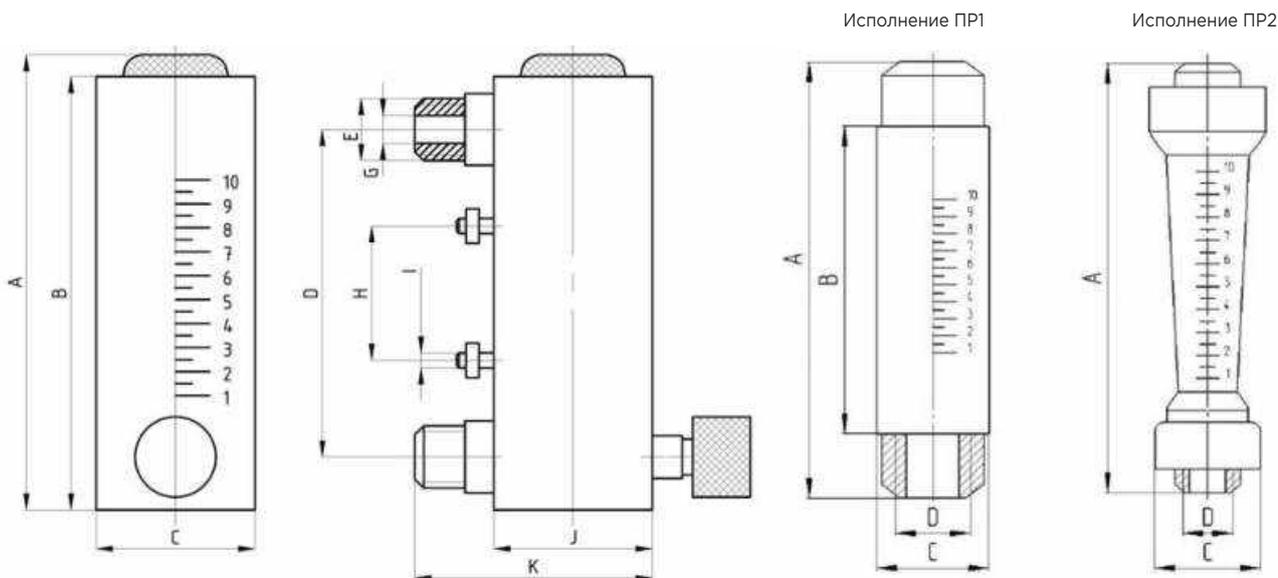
Габаритные и присоединительные размеры ротаметров ЭМИС-МЕТА 211, 211-Р панельный тип (ПА)
